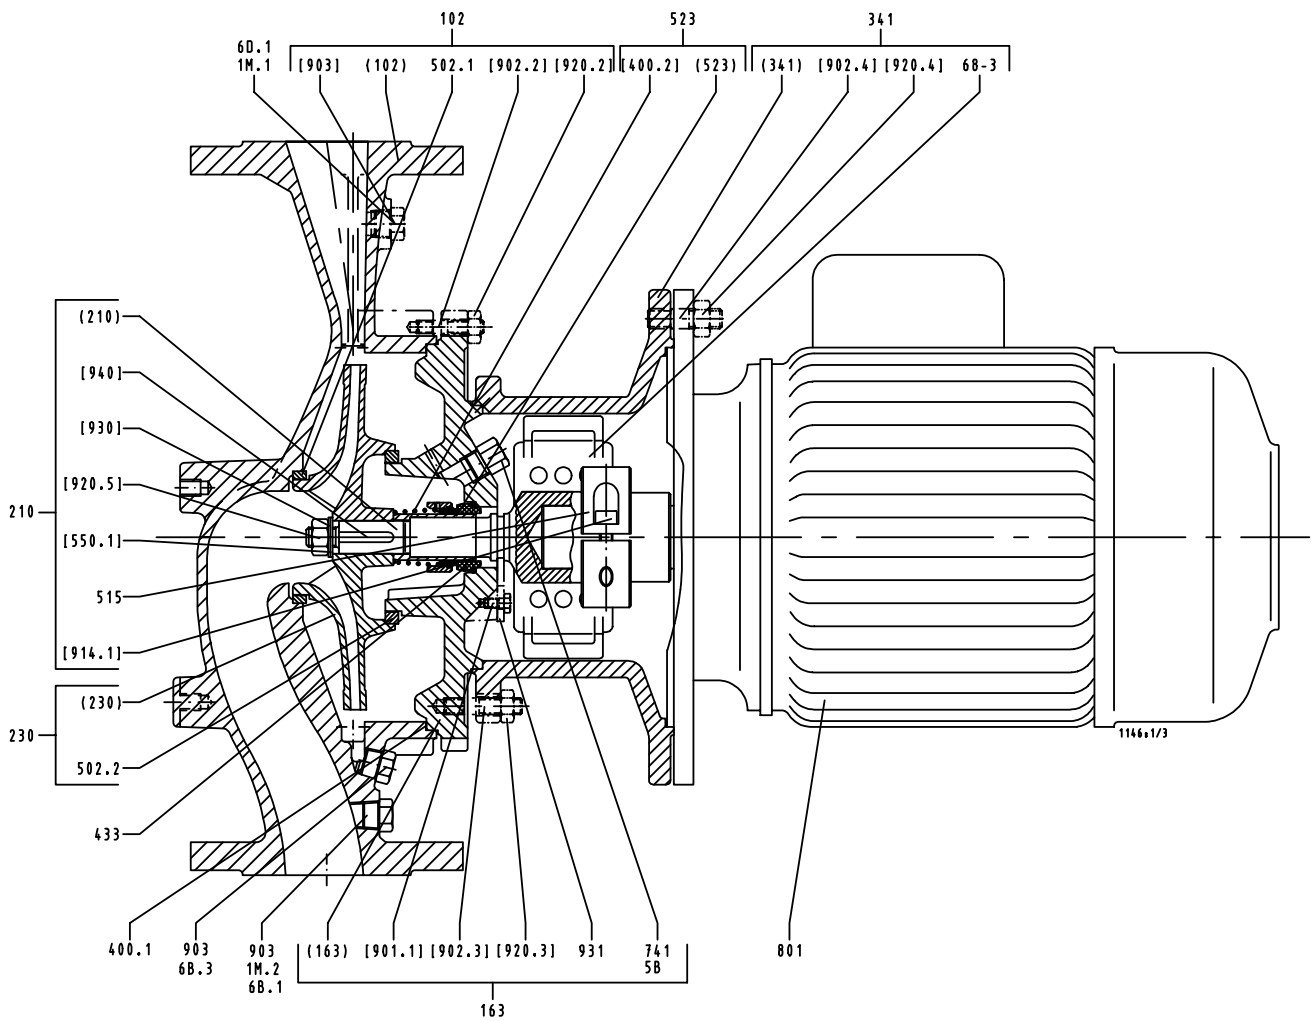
Стандартное торцевое уплотнение и резьбовая напорная крышка
